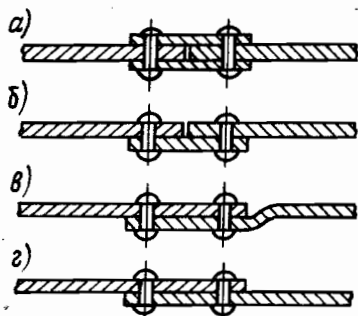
Типы заклепочных соединений: а — внакрой; б — внакрой с фланжировкой; в — встык на одной стыковой планке; г — встык на двух стыковых планках
